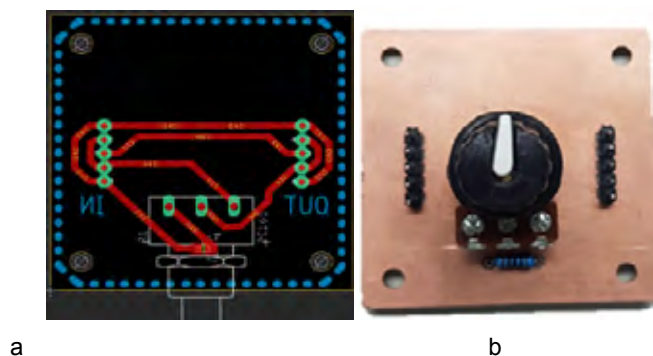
Módulo de perilla: a) Diseño de PCB, b) Implementación de PCB.
